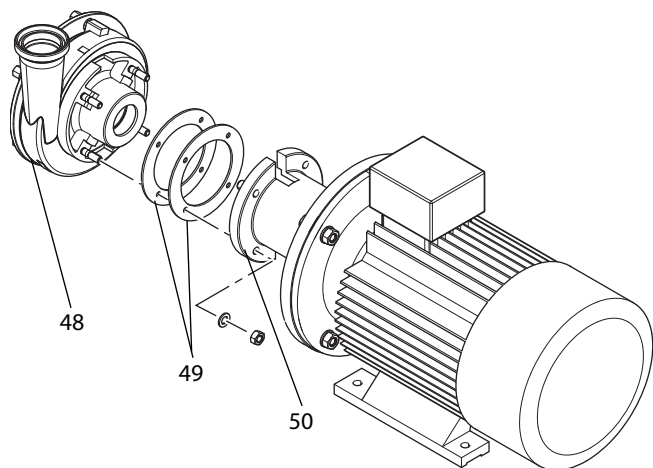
Ajustar a medida da folga em caso de junta flangeada
